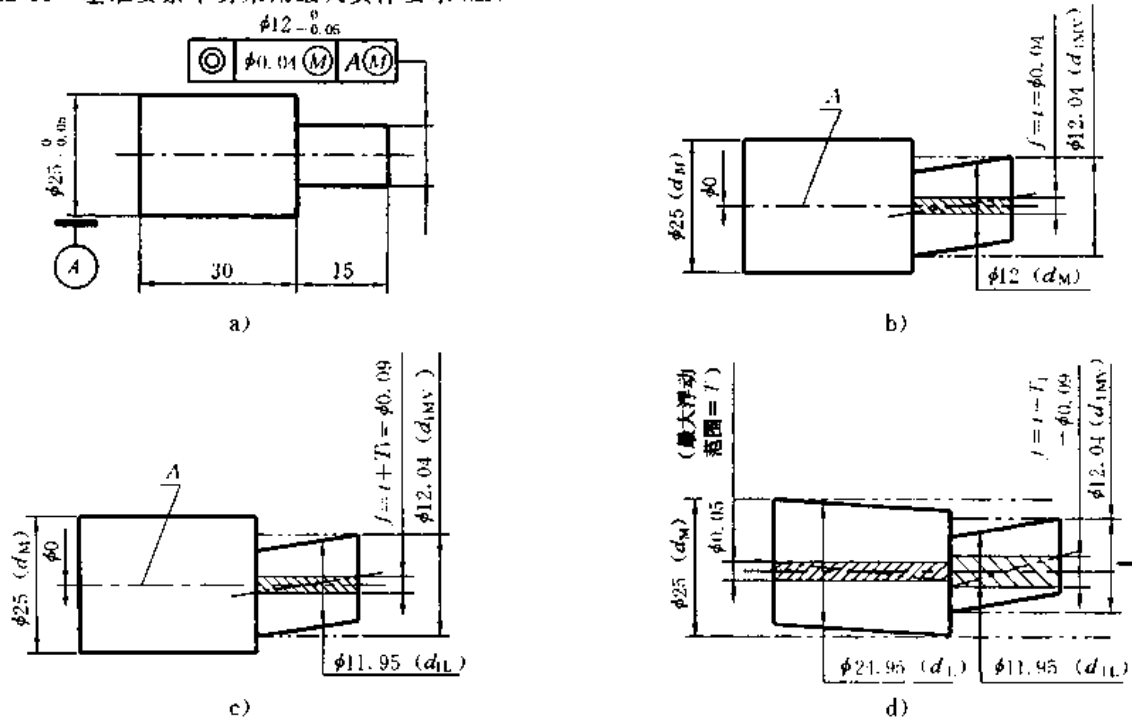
最大实体要求应用于同轴度公差和基准要素
